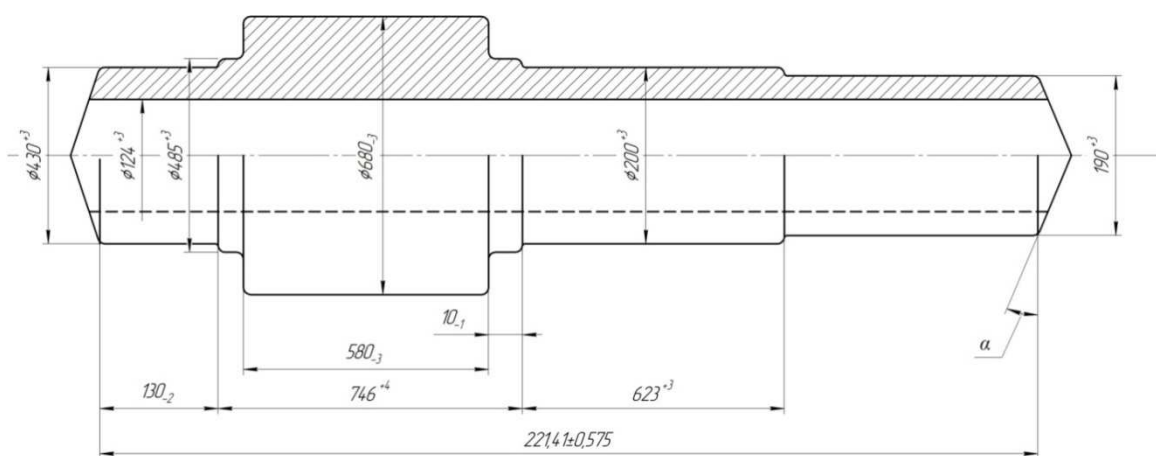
Вид пустотелой заготовки, полученной из проката квадратного сечения
